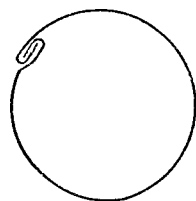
Поперечный разрез корпуса сборной жестяной банки со швом «взамок»
